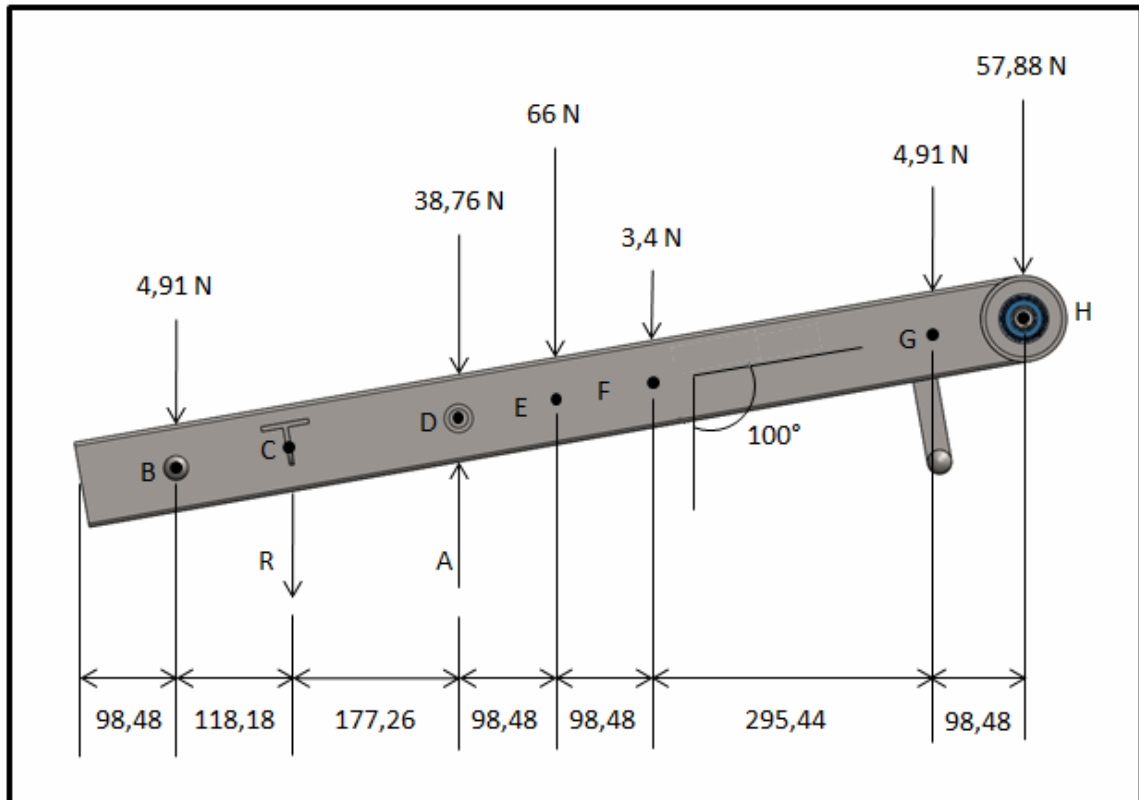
Distribución de cargas sobre la viga ó brazo horizontal en posición inicial (distancia en mm y cargas en newton) [Fuente: propio].
